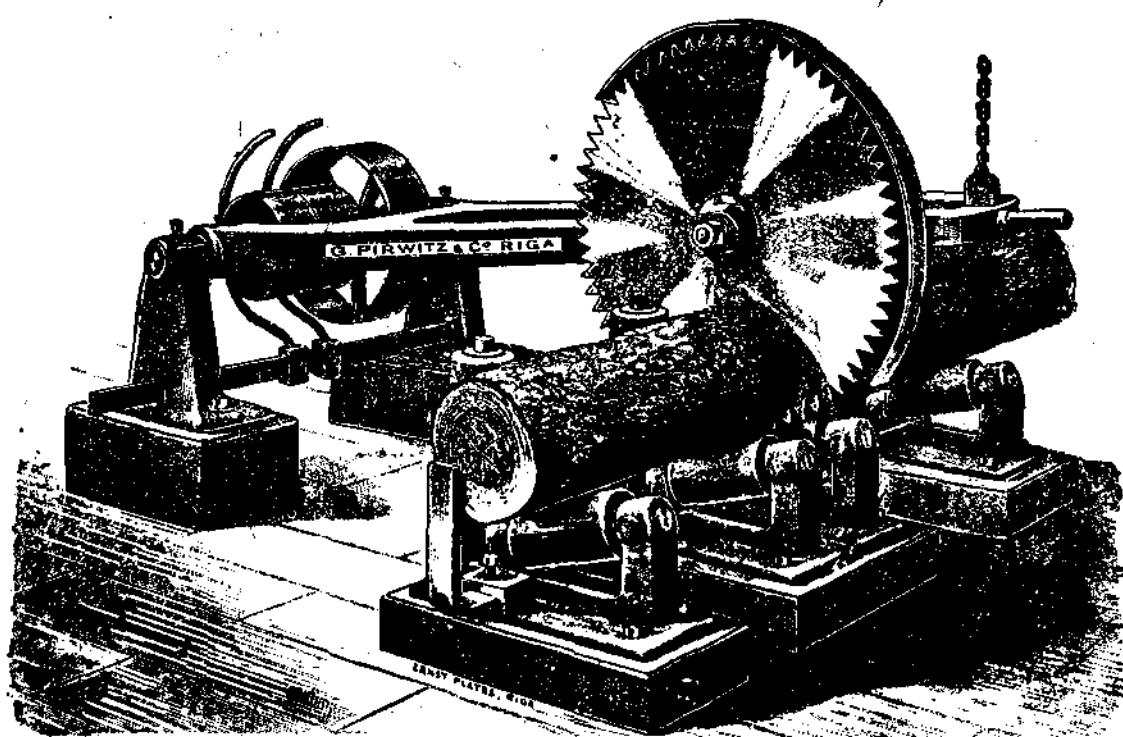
Приводный балансирующий станок с круглой пилой для поперечного распиливания бревен.
